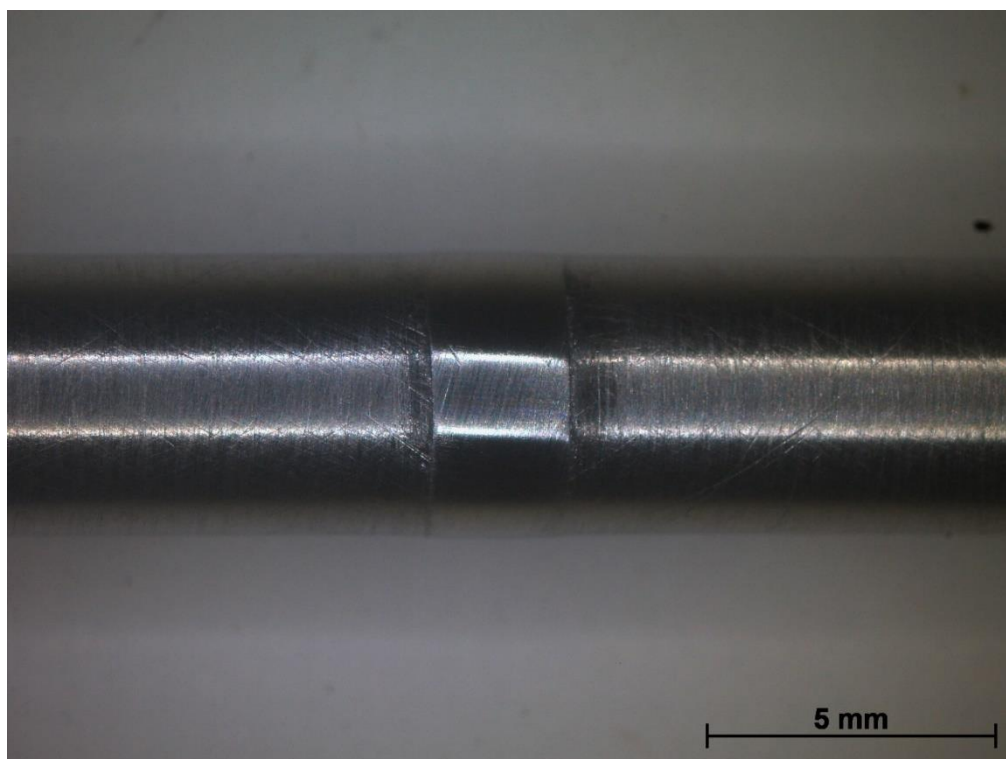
Local da junta soldada após o acabamento final.
